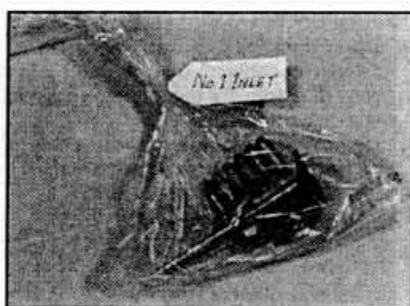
D.29. Использование маркированного полиэтиленового пакета для хранения деталей клапана.
